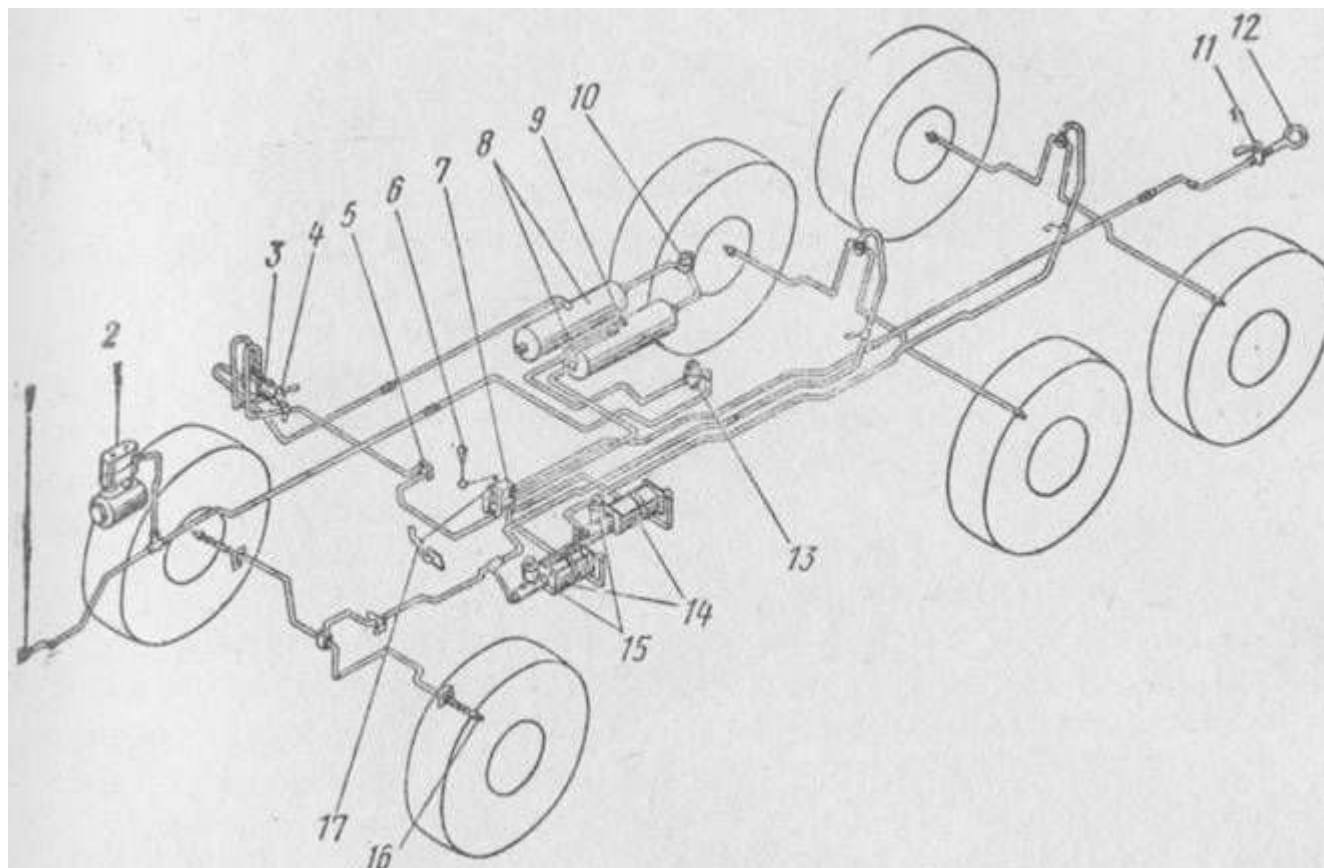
Схема компоновки прибора пневмогидравлического привода тормозов:
